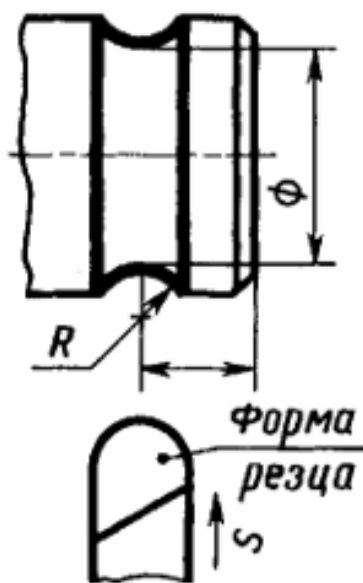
Схема простановки размеров полукруглой канавки-фиксатора и положение резца
